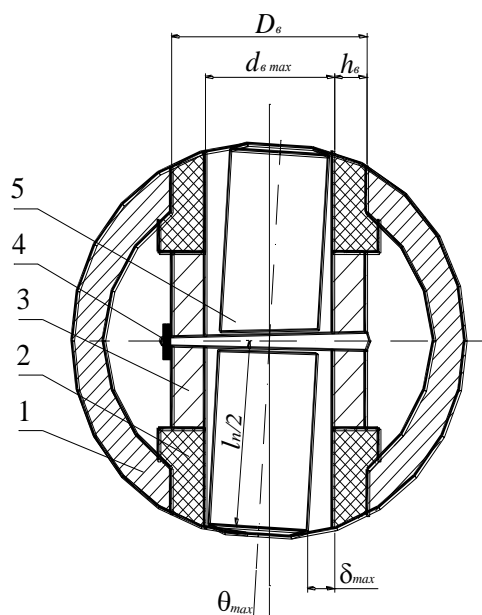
Розрахункова схема шарнірного з'єднання гвинтових секцій: 1 - циліндрична втулка; 2 - антифрикційна втулка; 3 - квадратний валець; 4 - штифт; 5 - циліндричний палець
